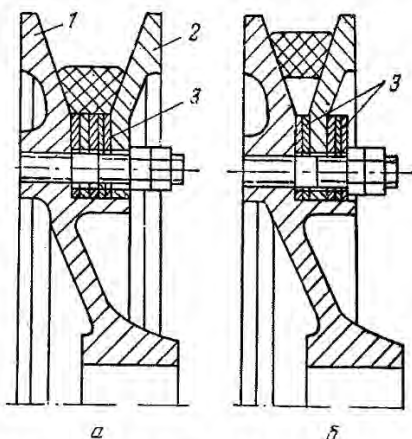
Регулировка натяжения приводного ремня компрессора:
